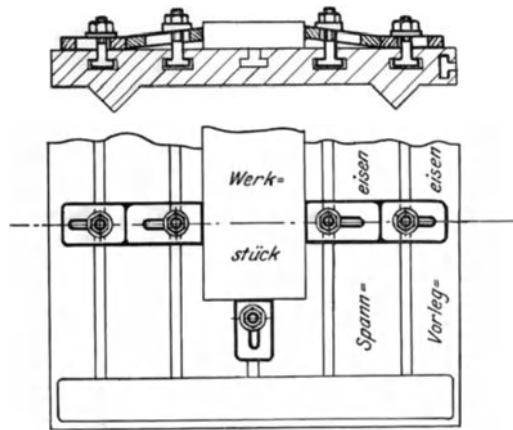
u. 152. Eine ältere Aufspannart für Hobelmaschinen.
